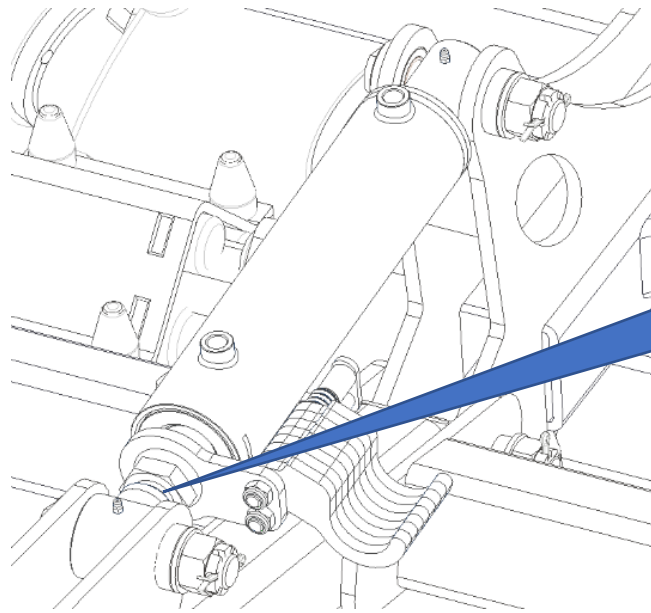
Vue du vérin avec écrou pour la mise à niveau de la machine.
